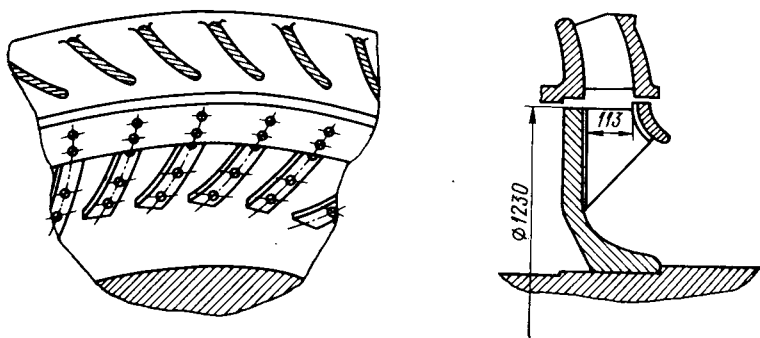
Центробежный компрессор с загнутыми назад лопатками
